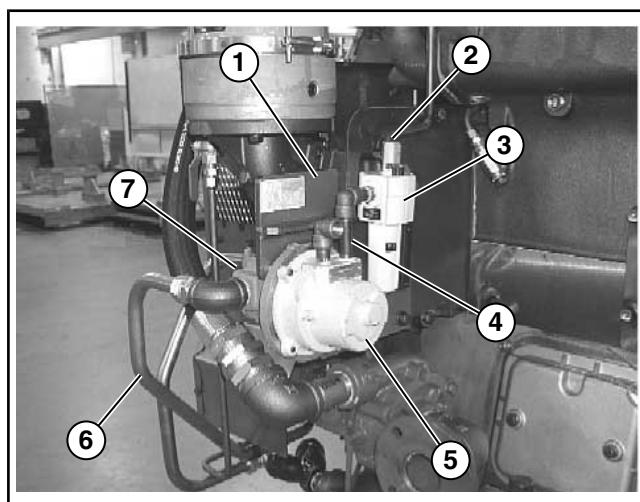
Насос и двигатель предпусковой смазки в сборе
